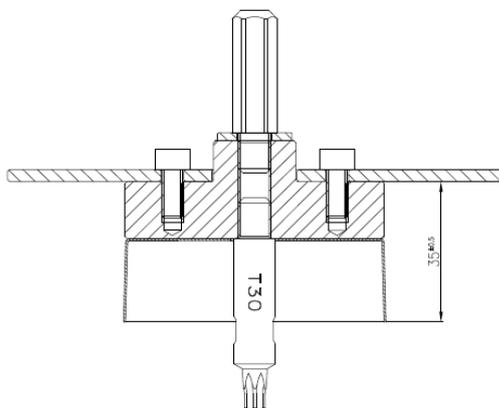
ejotherm STR U Montagewerkzeug Typ "L" für Dämmstoffdicken ab 100 mm
